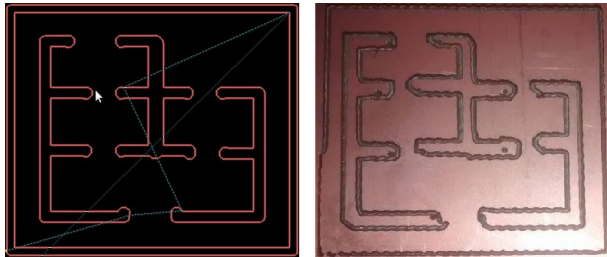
Comparación entre el diseño de una PCB frente al producido por la máquina
